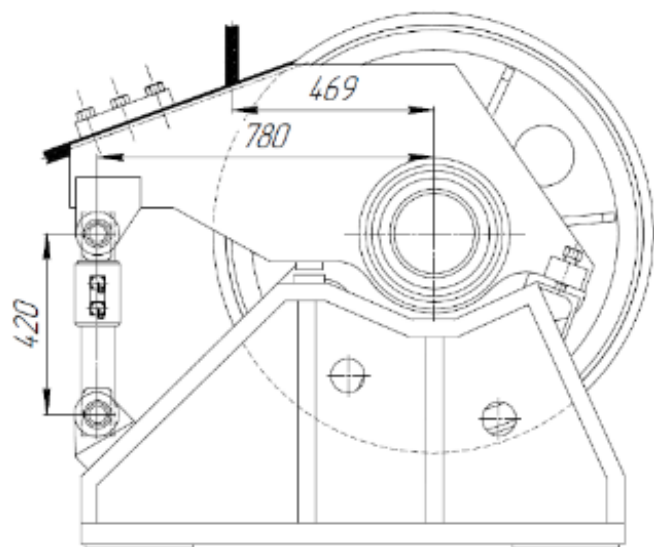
Габаритные и присоединительные размеры ДН-130В(Р)
